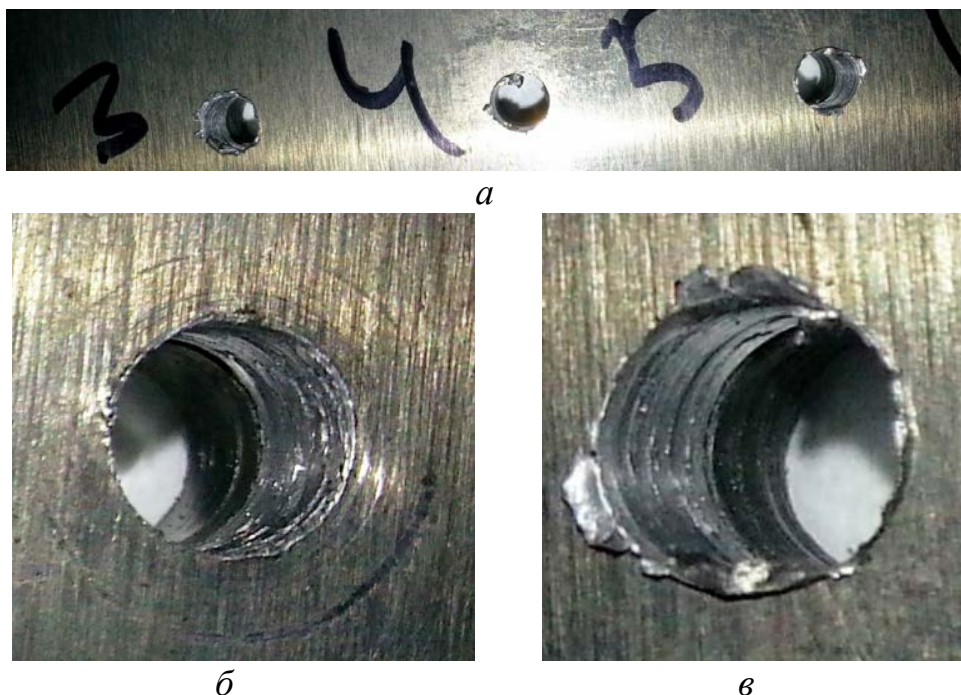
Дефекты при разделке металла без охлаждения режущего инструмента; *а* – ряд отверстий в металлической пластине; *б* – кромка и внутренняя поверхность отверстия на входе в металл; *в* – кромка и внутренняя поверхность отверстия на выходе из металла
